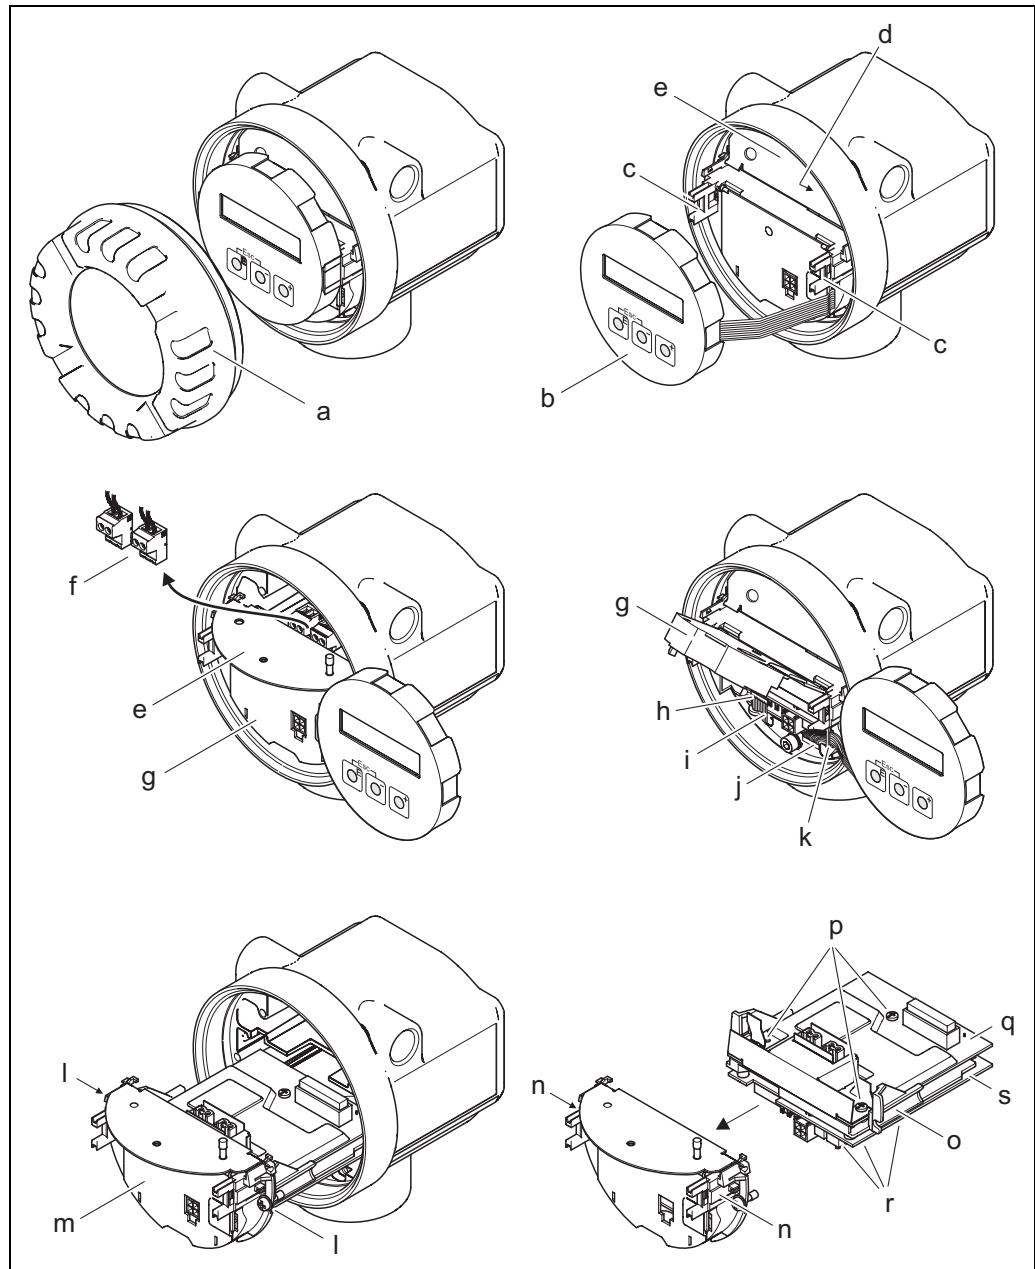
Instalação e remoção de placas eletrônicas das versões não-Ex, Ex-i/IS e Ex-n
